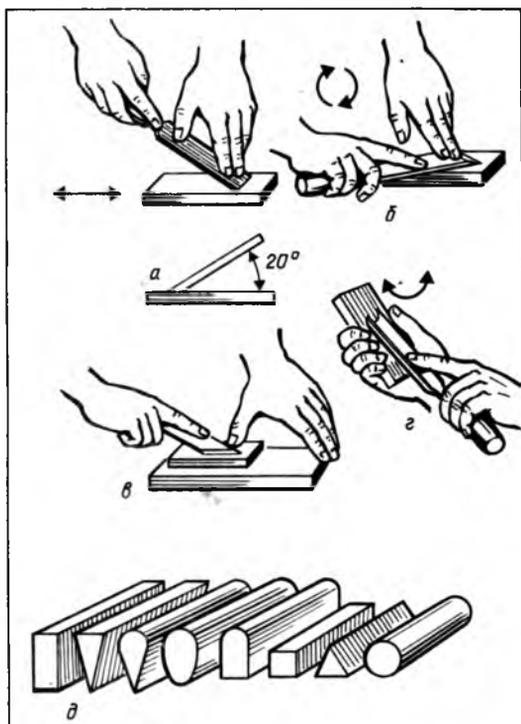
Заточка и правка стамесок: а, б — заточивание прямой стамески со стороны фаски и с лицевой стороны; в — положение ножа-косяка при заточивании на мелкозернистом бруске; г — правка полукруглой стамески на весу; д — оселки для правки резчицких стамесок
